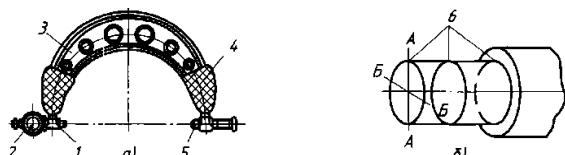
Скоба с отсчетным устройством (а) и определение посадочных размеров конца вала (б):
